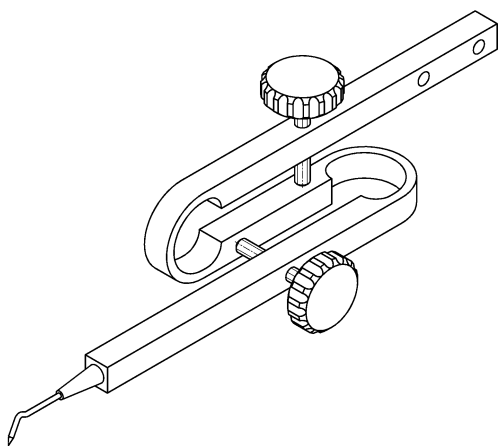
Мікроманіпулятор, виготовлений з пруткового матеріалу
